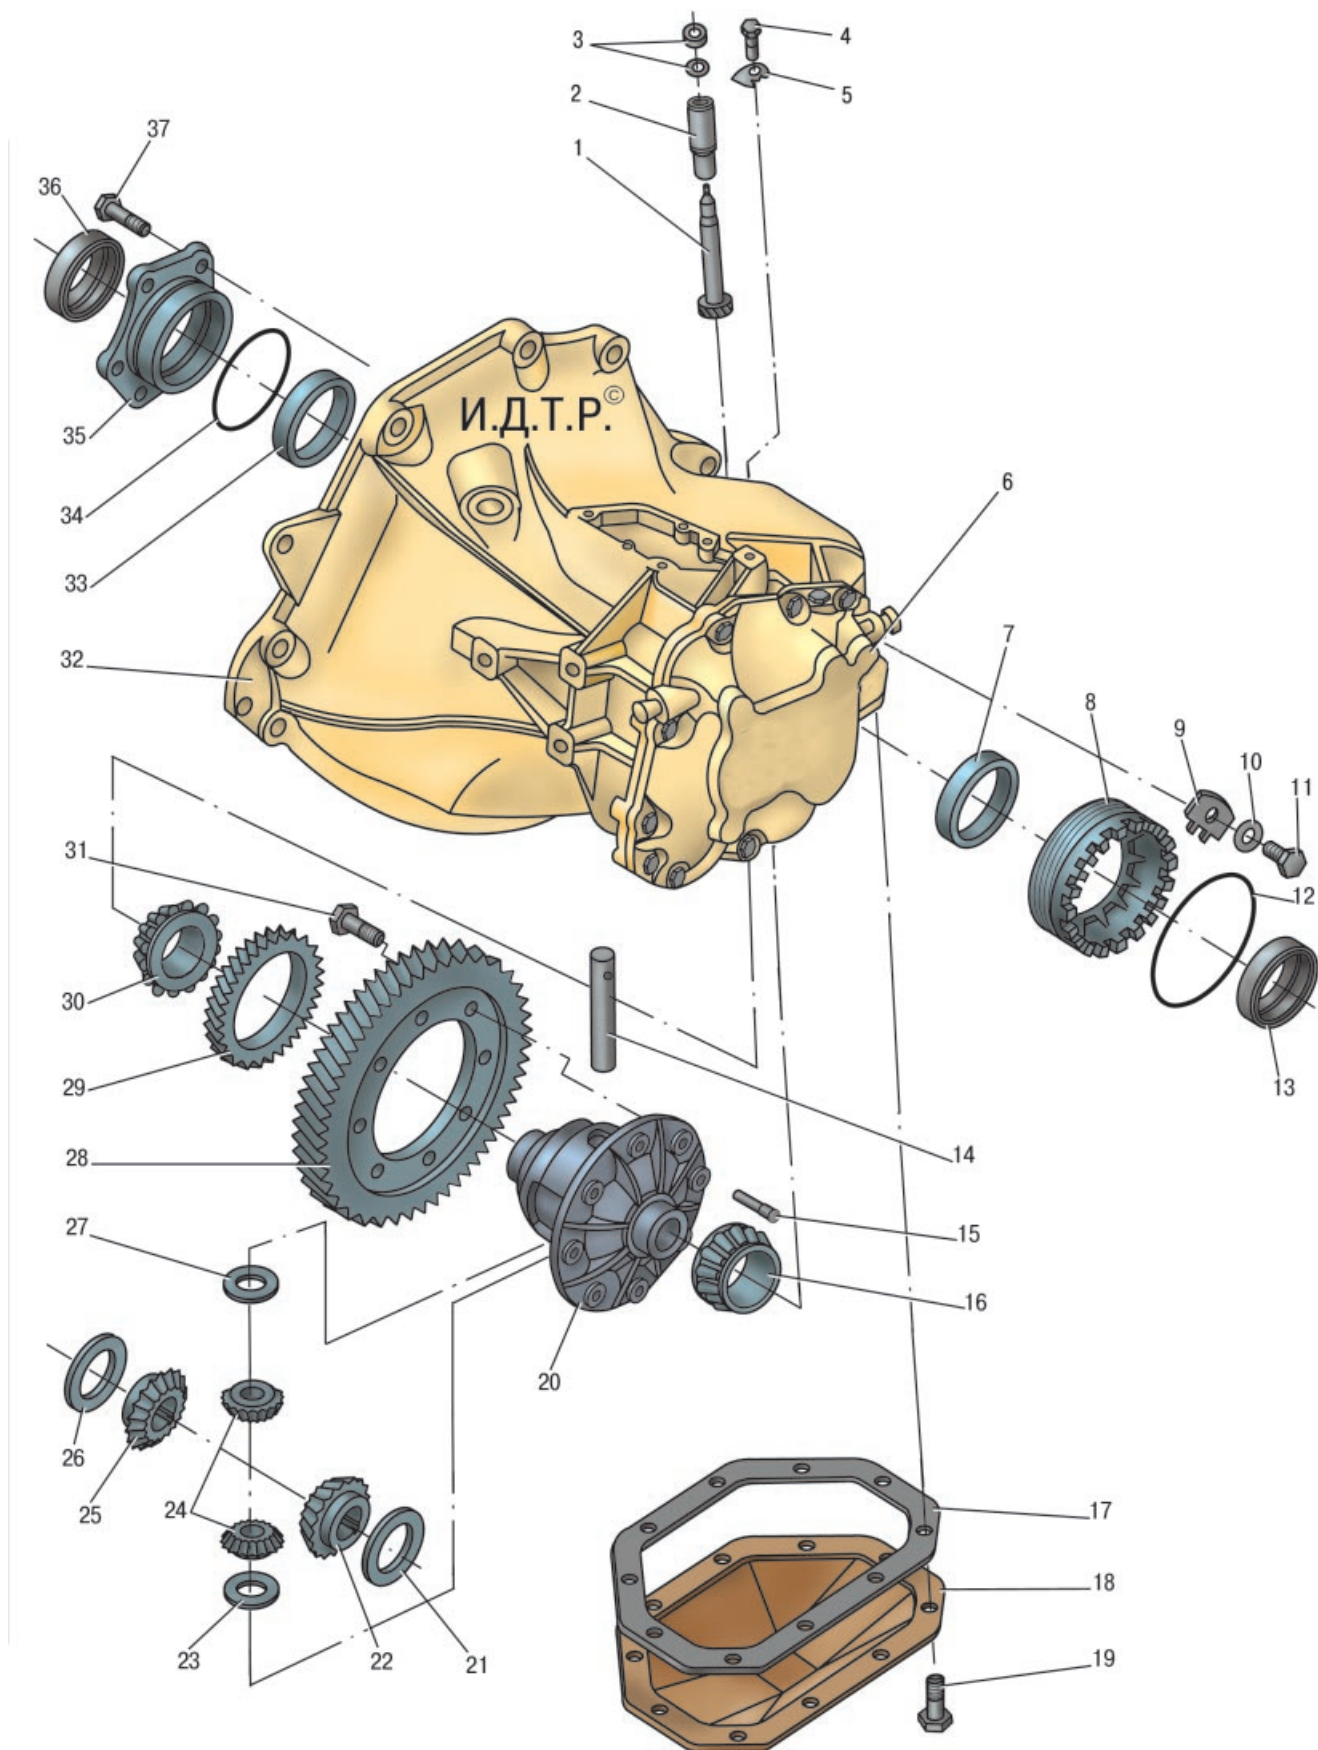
Главная передача и дифференциал: 1 – вал-шестерня редуктора привода спидометра; 2 – корпус редуктора привода спидометра; 3, 12, 34 – уплотнительные кольца; 4, 11, 19, 31, 37 – болты; 5 – стопорная пластина; 6 – задняя крышка коробки передач; 7, 33 – наружные кольца подшипников дифференциала; 8 – регулировочная гайка подшипников; 9 – пластина фиксатора; 10 – шайба; 13, 36 – сальники; 14 – ось сателлитов дифференциала; 15 – фиксатор оси сателлитов; 16, 30 – конические роликовые подшипники дифференциала; 17 – прокладка; 18 – нижняя крышка коробки передач; 20 – корпус дифференциала; 21, 26 – упорные шайбы; 22, 25 – полуосевые шестерни; 23, 27 – упорные шайбы сателлитов; 24 – сателлиты; 28 – ведомая шестерня главной передачи; 29 – ведущая шестерня привода спидометра; 32 – картер коробки передач; 35 – правая крышка подшипников дифференциала
